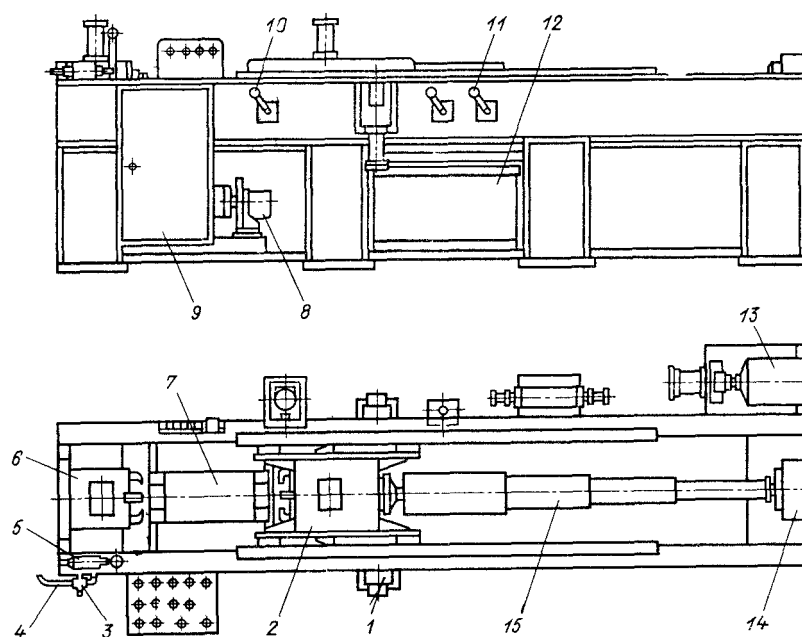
Стенд для испытания подъемного механизма (модель С416-726)
